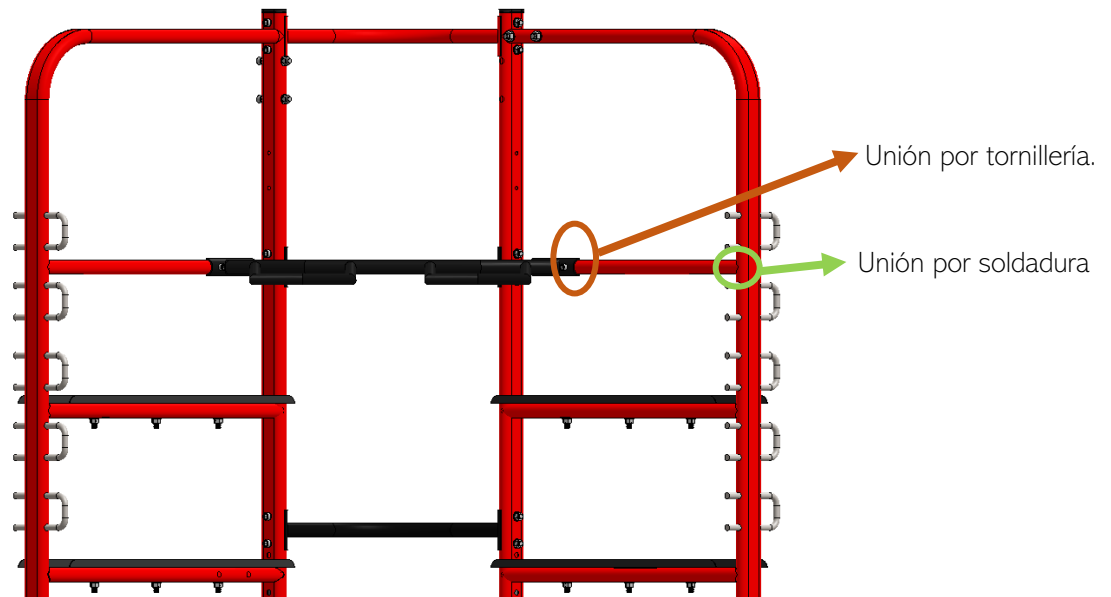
Soldadura y uniones del subconjunto 4. Fuente: Elaboración propia
